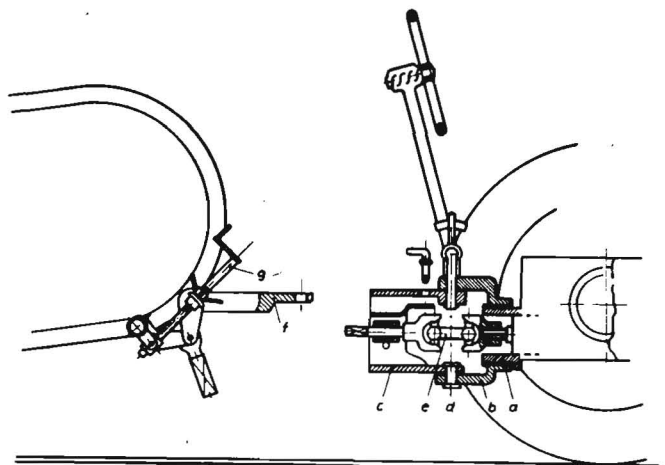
Kupplungsvorrichtung zur Steuerung und zum Anschluß des Frontbinders
